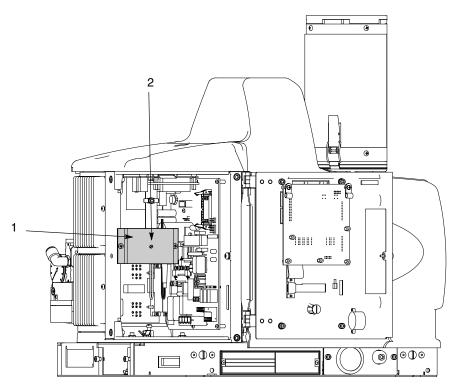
Position Verstärkerleuchte und Einstellschraube des Füllstandssensors
